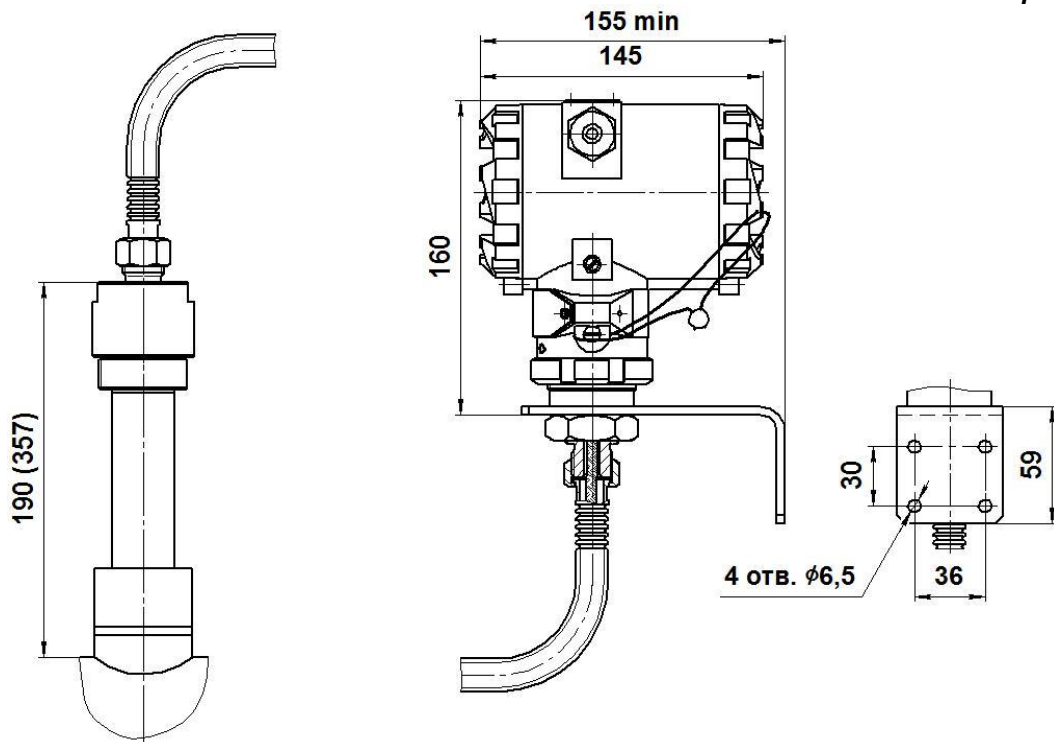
Размеры погружного преобразователя на давление 1,6 МПа
